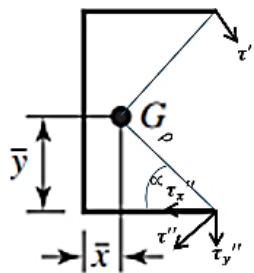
Análisis de la torsión en el cordón de soldadura del Elemento 6 [14].
